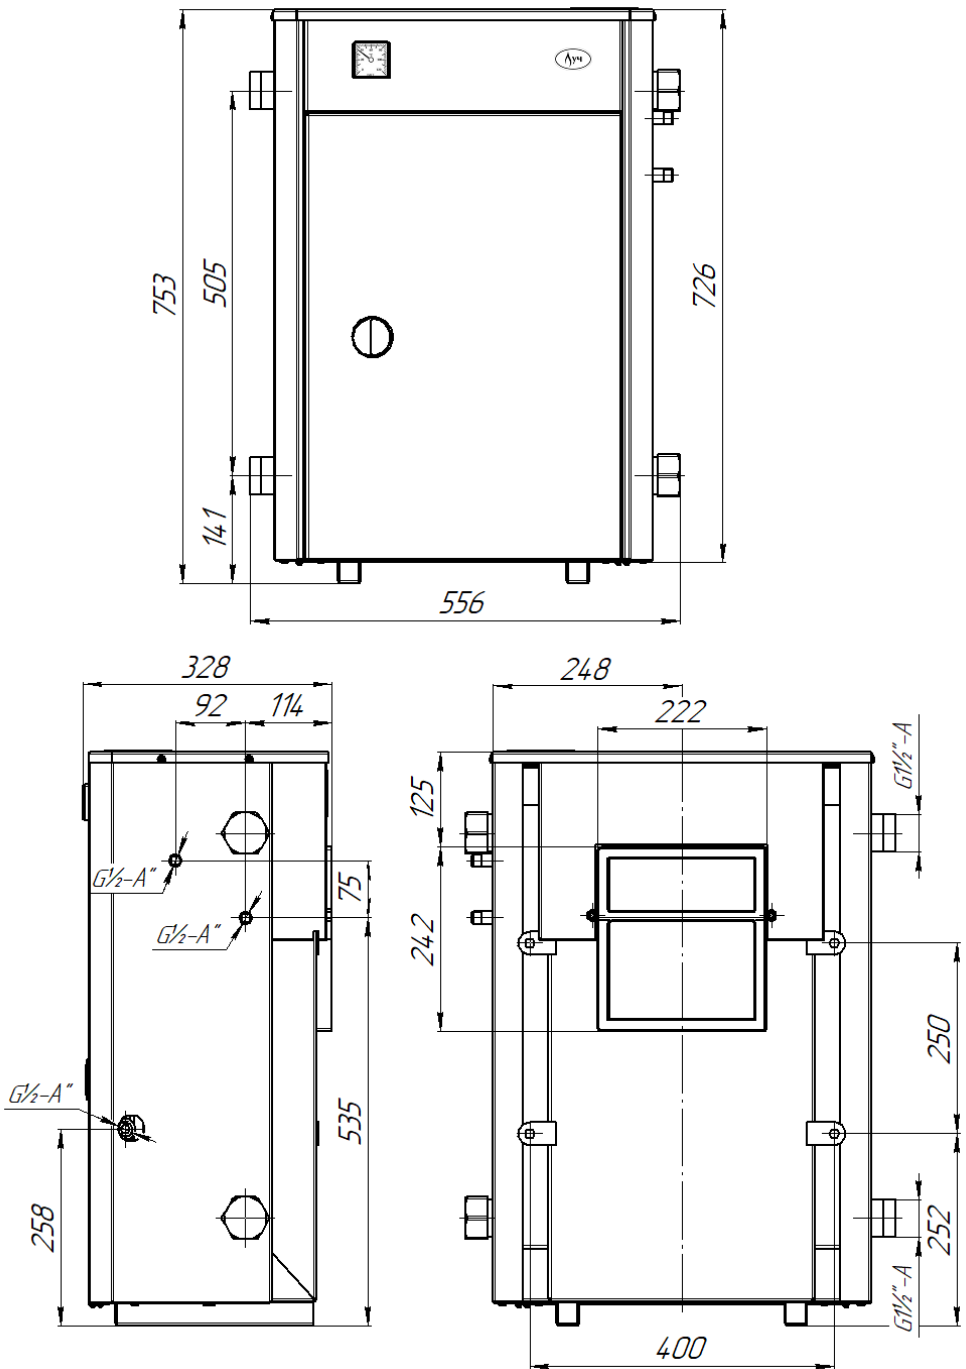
Габаритные и присоединительные размеры КСГ/КСГВ – 10/12П
